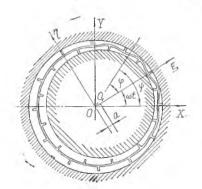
Упруго-демиферная опора: 1, 2 — упругие элементы; 3 — корпус опоры; 4 — втулка; 5 — подининик
